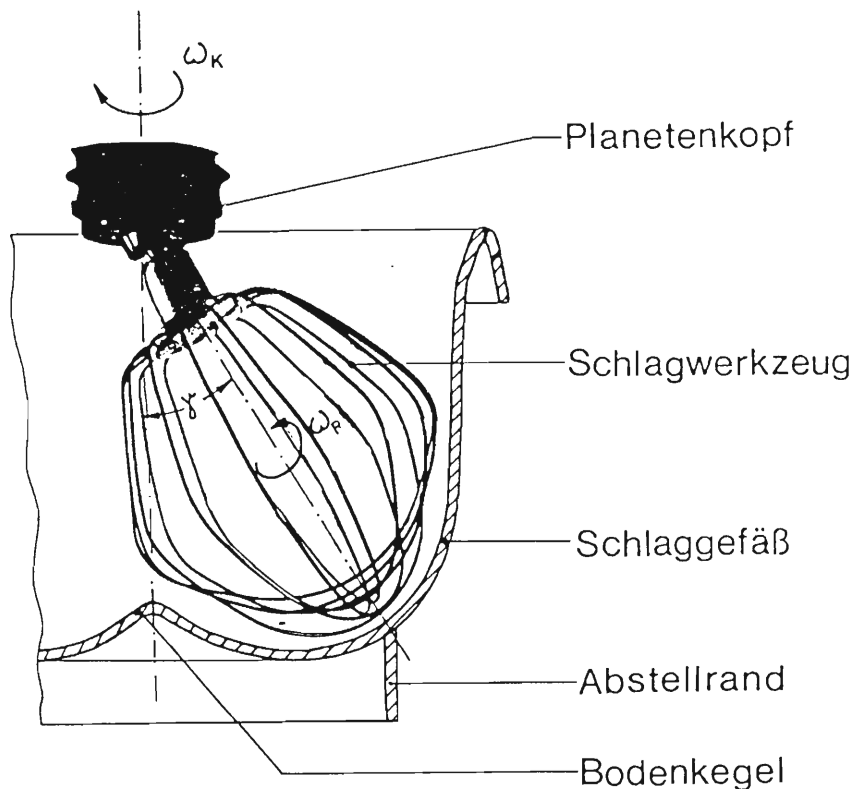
/15: Gut angepaßtes Schlagwerkzeug mit Schlaggefäß einer Klein-Küchenmaschine mit Planetenantrieb
